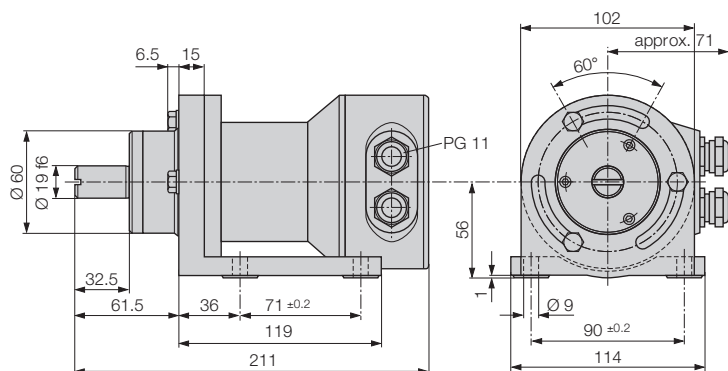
KINAX WT 707 с дополнительным редуктором, винтовыми клеммами, кабельными вводами и опорой.
